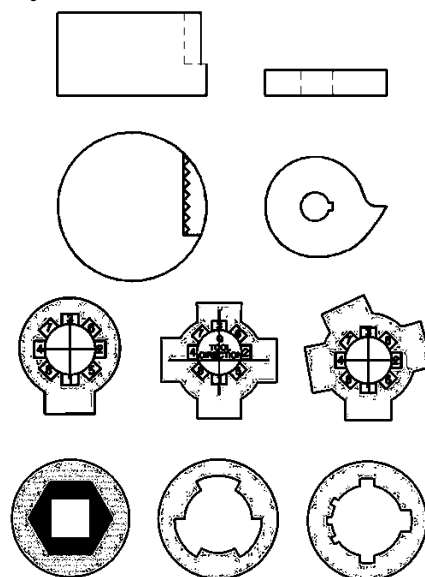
Варианты обрабатываемых форм профилей и поверхностей
